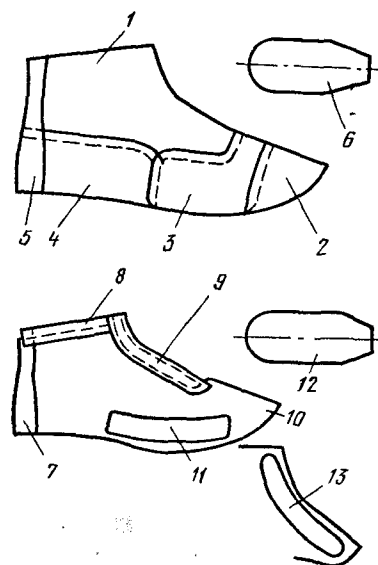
Схема сборки заготовки верха ботинок с настрочными союзками
